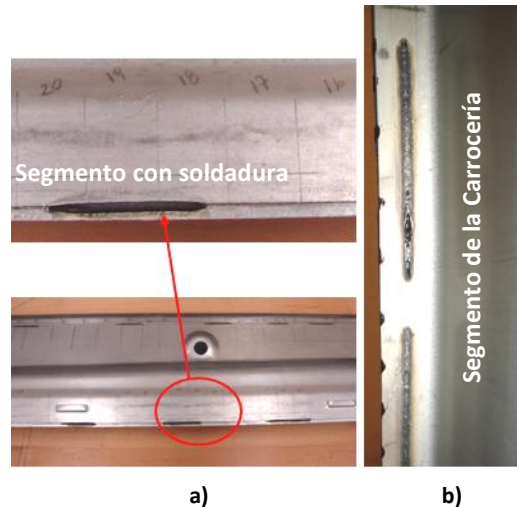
Soldadura láser en secciones de dos ensambles automotrices de láminas delgadas de acero.
